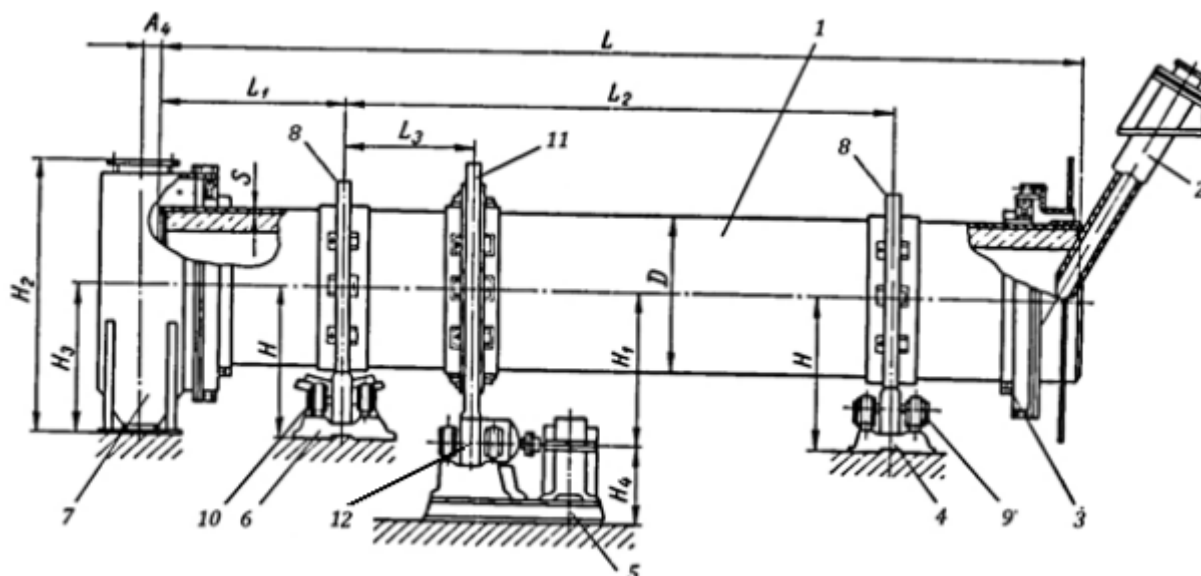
Схема двухопорного аппарата с вращающимся барабаном:
